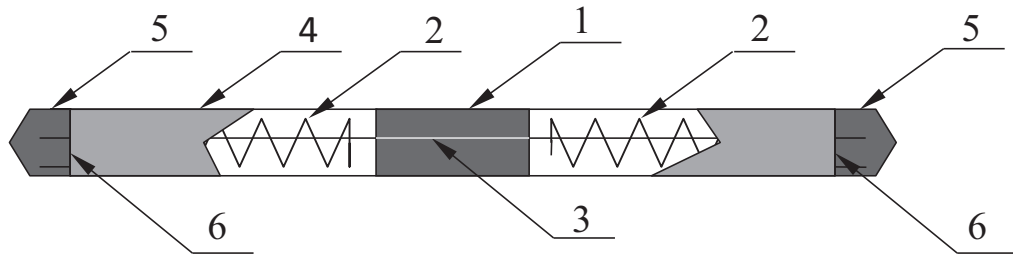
1- груз, 2- пружина, 3- металлический стержень, 4- пластиковый корпус, 5- наконечник, 6- крепеж.
